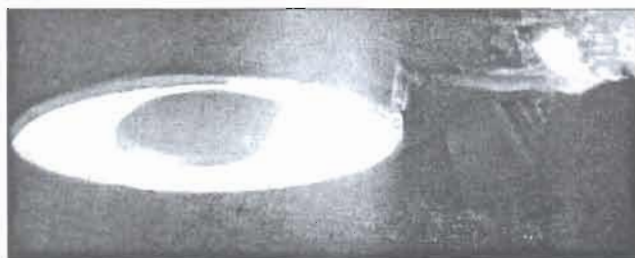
Процесс получения титановой трубной заготовки способом ЭЛПЕ
